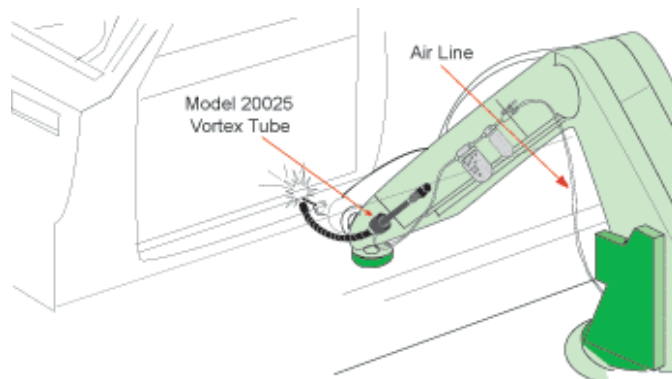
Enfriado de soldadura por puntos con Tubo Vórtex
